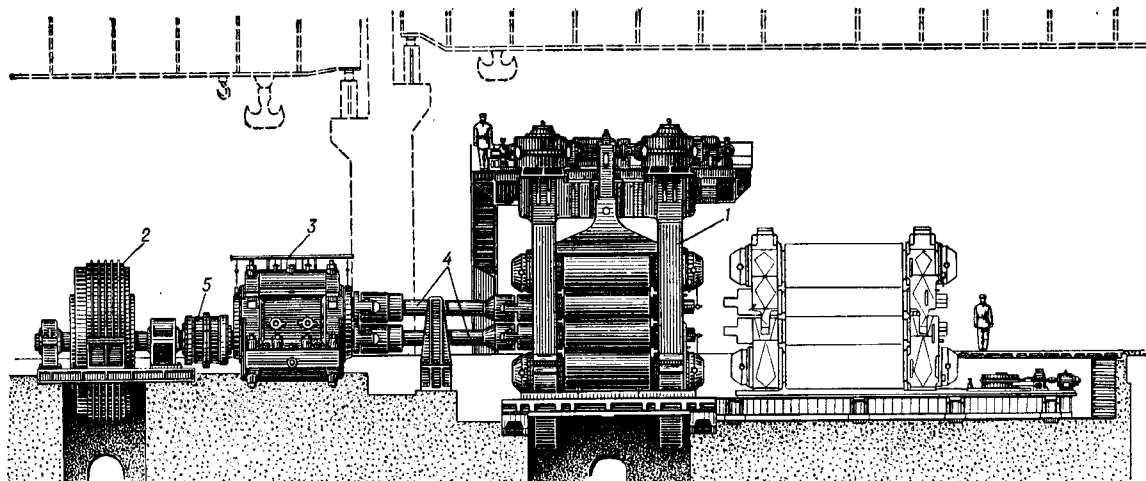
Главная линия четырёхвалкового стана для прокатки листов: 1 — рабочая клеть; 2 — электродвигатель; 3 — шестерённая клеть; 4 — шпиндели; 5 — муфта.
